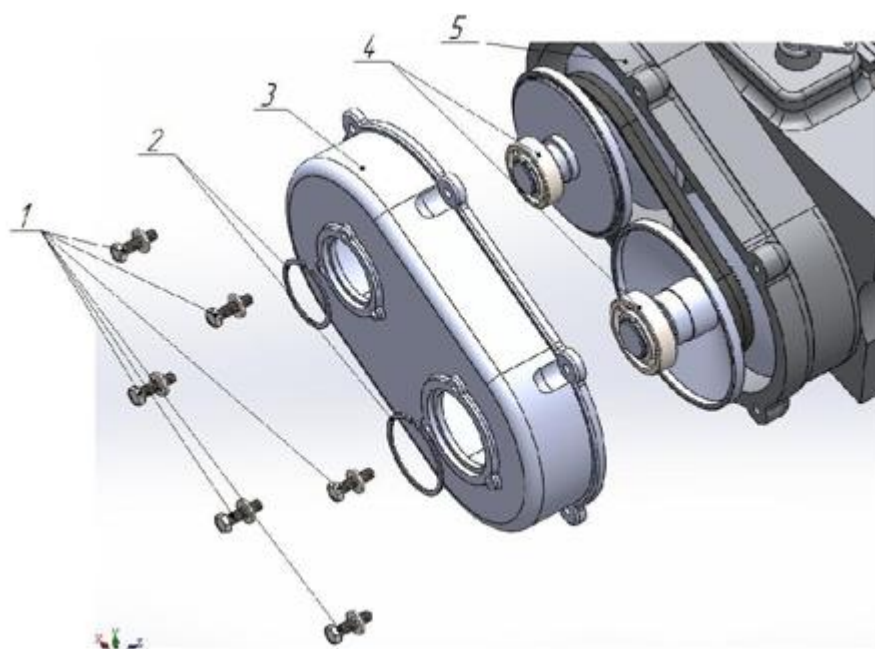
Клиноременная передача: 1 – крепежные винты; 2 – стопорные кольца; 3 – крышка вариатора; 4 – подшипники качения; 5 – корпус вариатора
